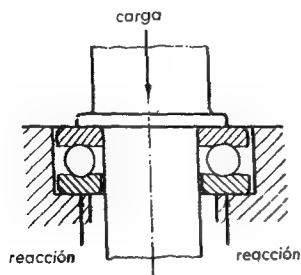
Cojinete para carga axial.* La carga no tiene componente radial.
